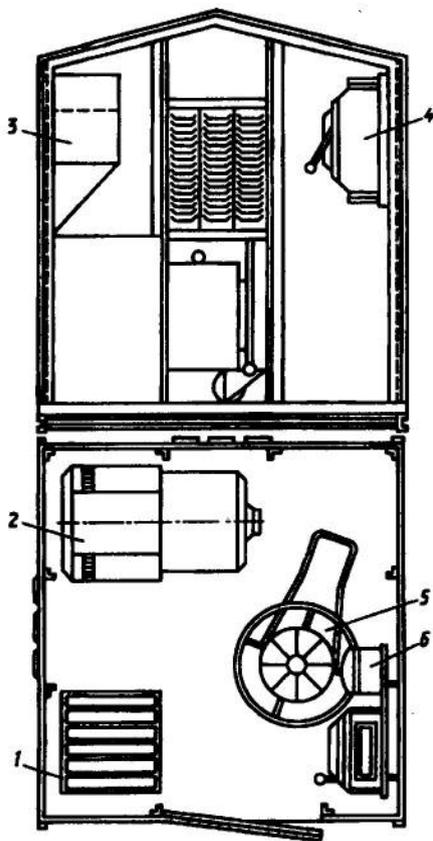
Пересувний контейнер з одним постом для механізованого зварювання:
